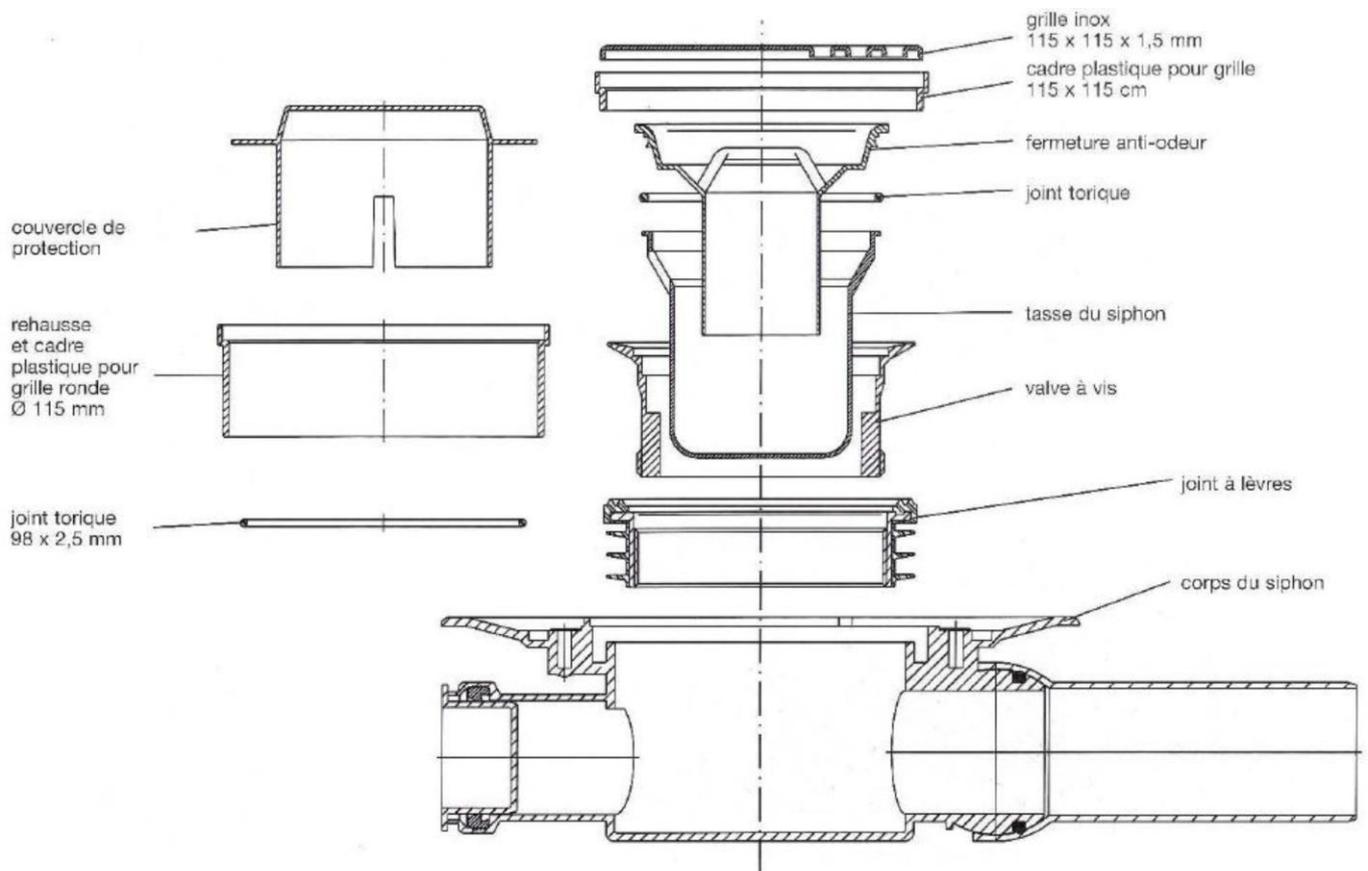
vue en coupe d'un siphon Fundo Primo ou Fundo Ligno plus
